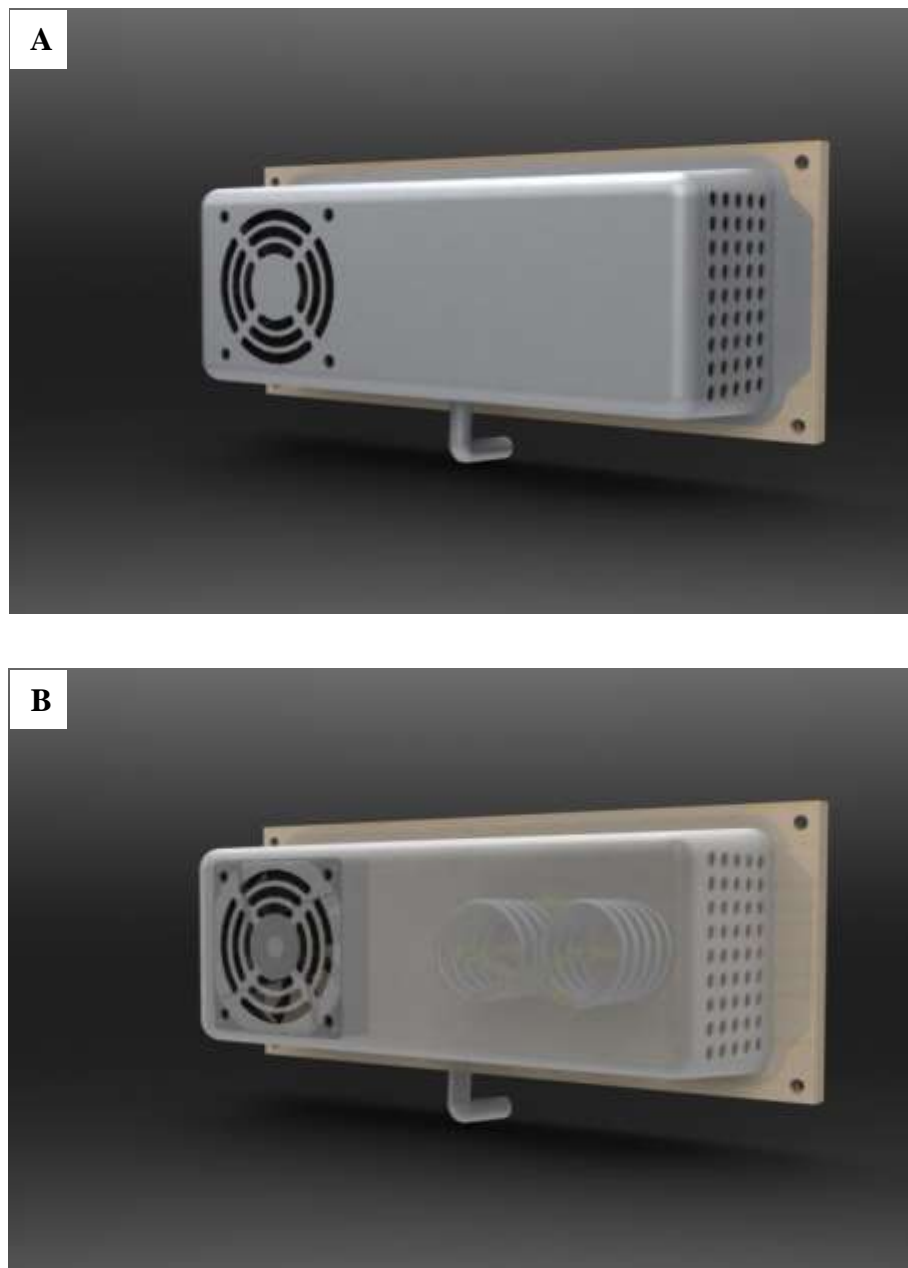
Sistema de refrigeração. Vista externa (A). Detalhes internos (B). Ilustração: O Autor
